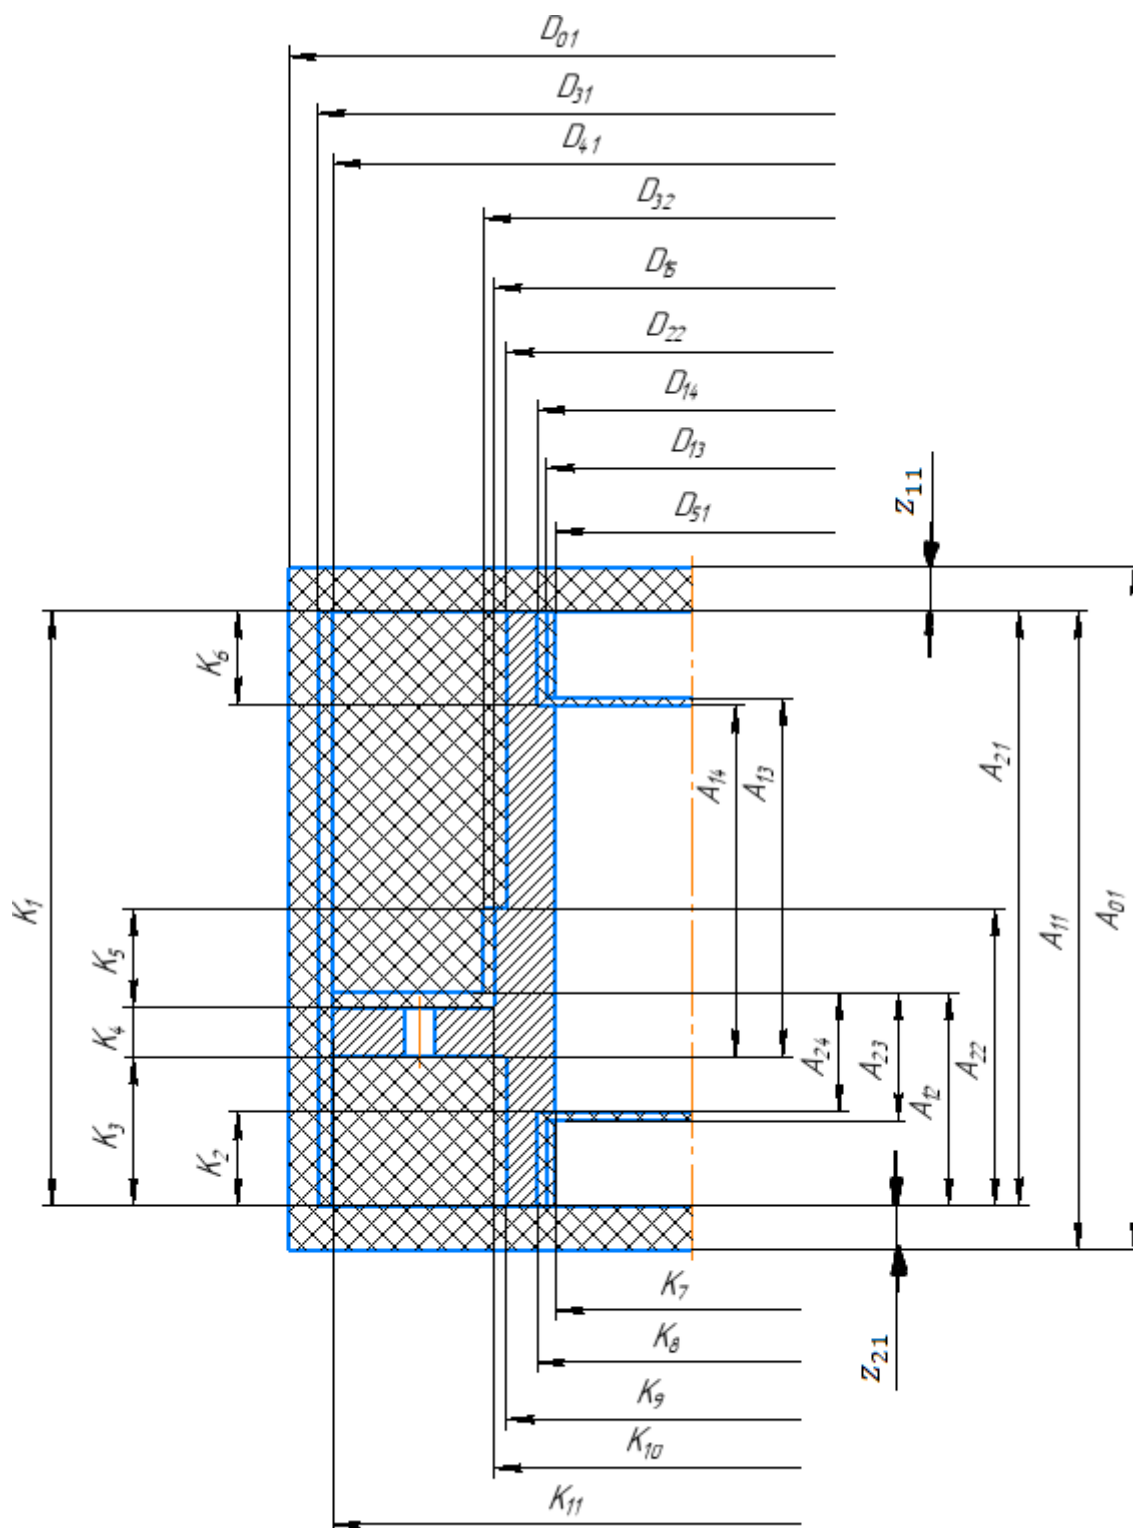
Размерная схема технологического детали «Втулка подшипниковая»
